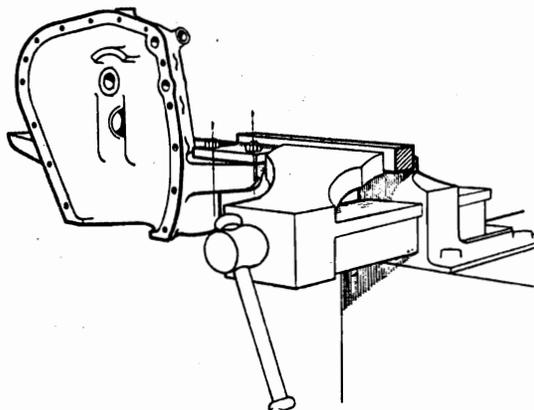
FIXATION DU CARTER ARRIÈRE DANS L'ÉTAU (4° VUE)
